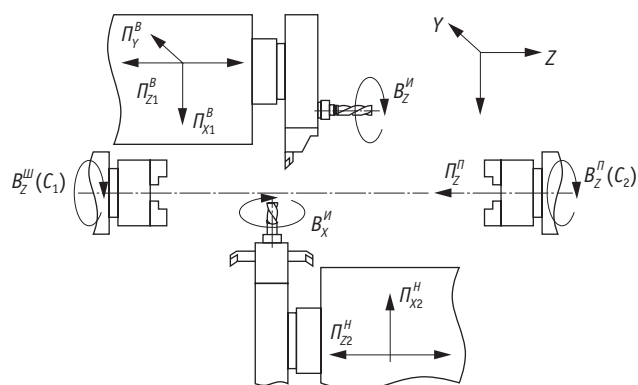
Формообразующие движения рабочих органов токарного обрабатывающего центра WT-150
